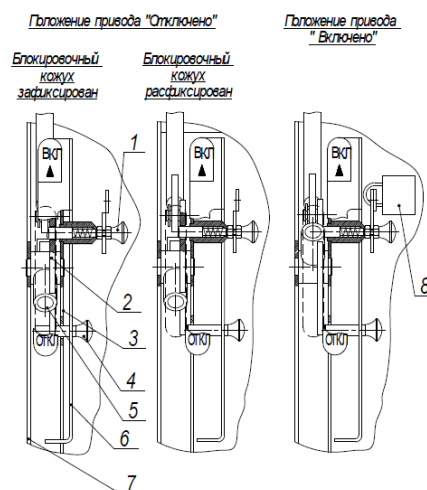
Привод заземлителя: 1 – фиксатор привода, 2 – поворотный диск, 3 – панель привода, 4 – фиксатор кожуха, 5 – гнездо привода, 6 – кожух блокировочный, 7 – станка шкафа боковая, 8 – замок навесной
